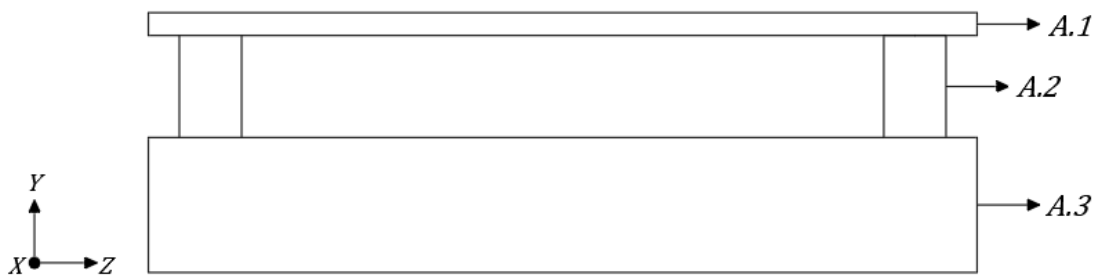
Vista frontal de la base superior de la máquina dobladora de placas de fijación.
